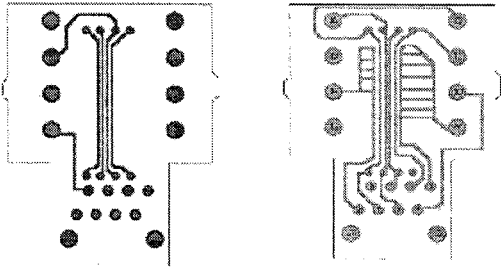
개발된 인핸스드 카테고리 5급 모듈라잭 PCB 패턴
